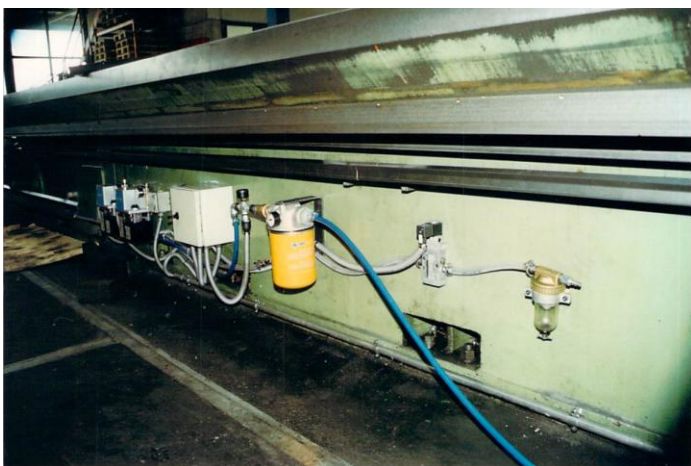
Die Einspeisung mit einer Filtrierung und der Steuerkasten.
